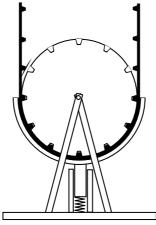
Подпружиненный ограничитель хода зубчатого ремня
